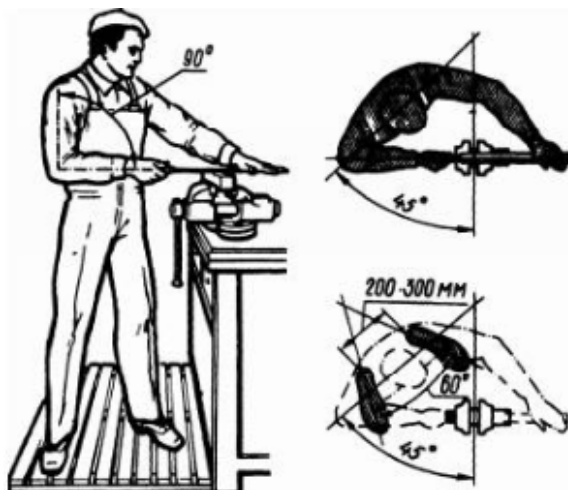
Положения рук, корпуса и ног при опиловании
